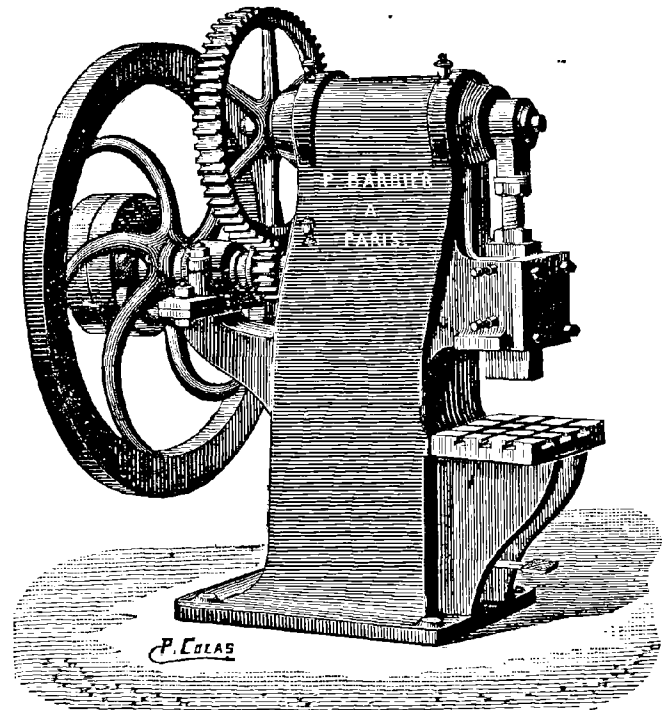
Machine à découper à excentrique de M. Barbier.
